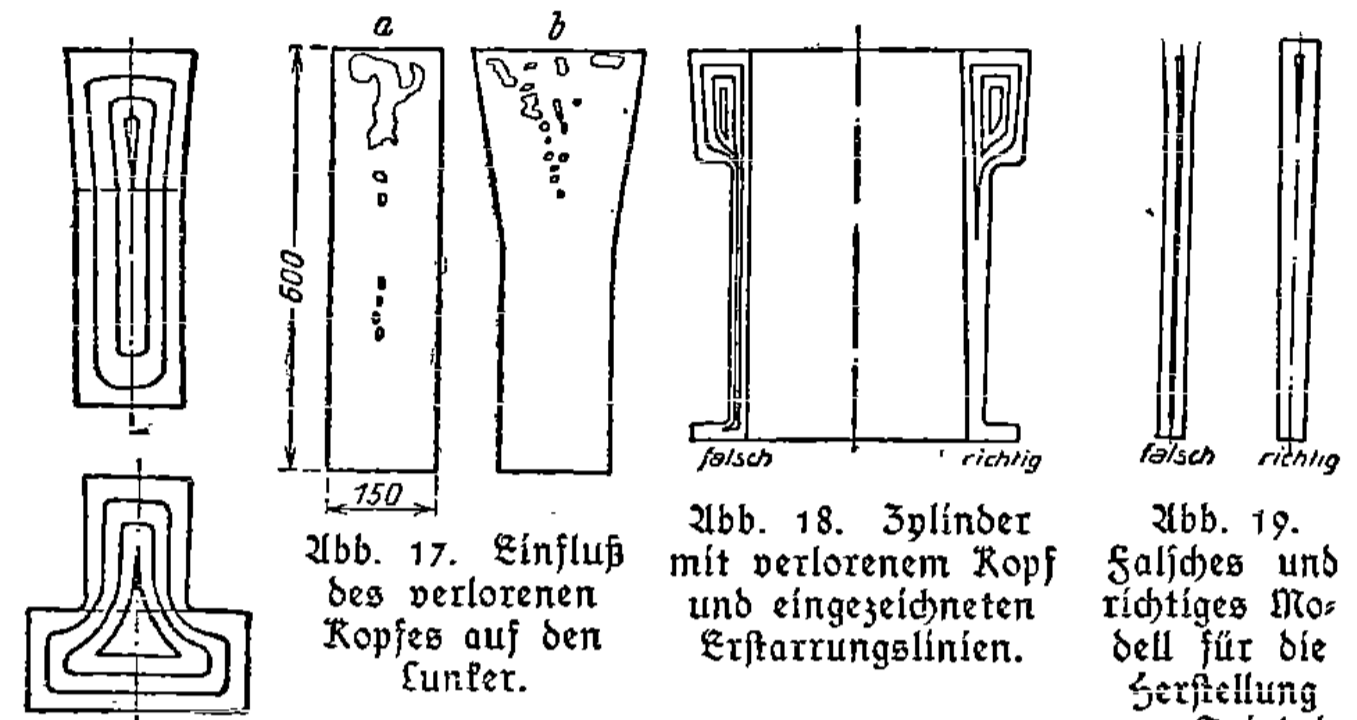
Dasselbe Stück flach und hochkant gegossen.
